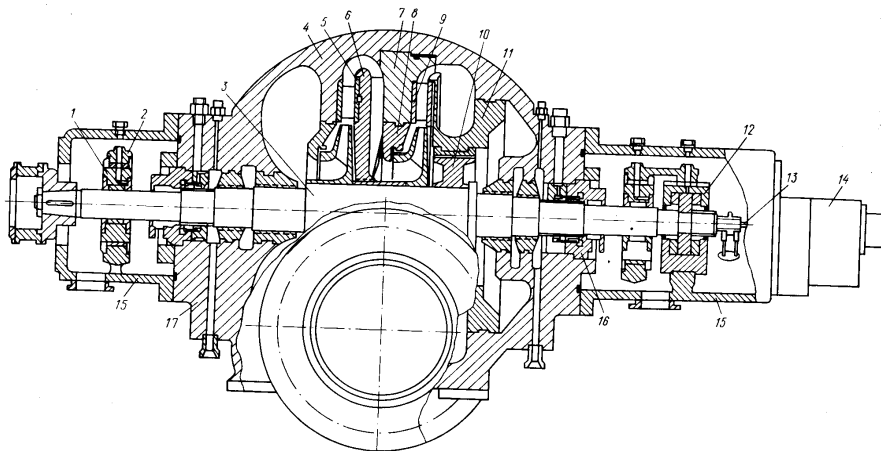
Нагнетатель ГПА: 1 – опорный подшипник; 2 – крышка подшипника; 3 – ротор; 4 – верхняя часть корпуса; 5 – диффузор; 6 – обратный направляющий аппарат; 7 – диафрагма; 8 – подвод; 9 – диффузор второй ступени; 10 – разгрузочный барабан; 11 – улитка; 12 – упорный подшипник; 13 – датчик; 14 – маслонасос; 15 – крышка; 16 – уплотнение концевое; 17 – нижняя часть корпуса
